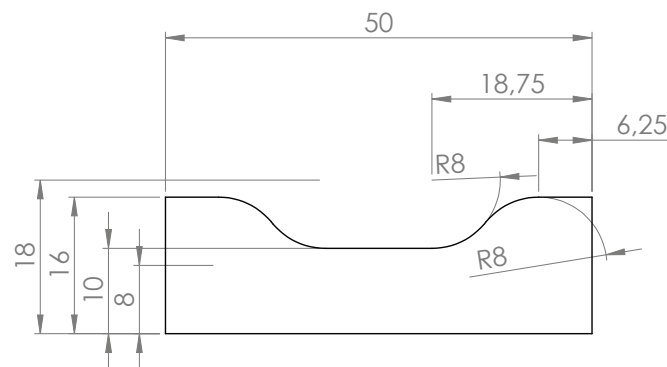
Mise en plan du substrat 3D V1 – vue de face
